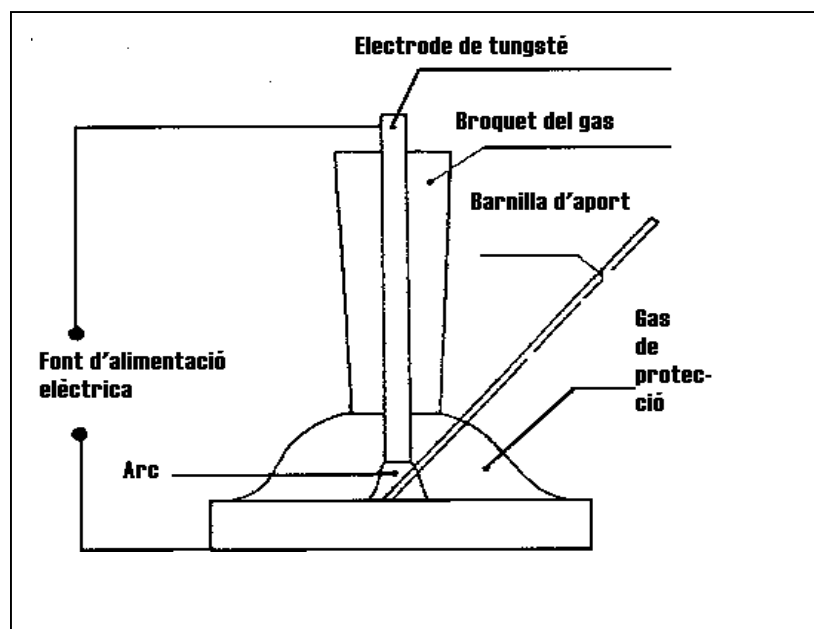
Esquema bàsic de soldadura amb gas inert (TIG)
